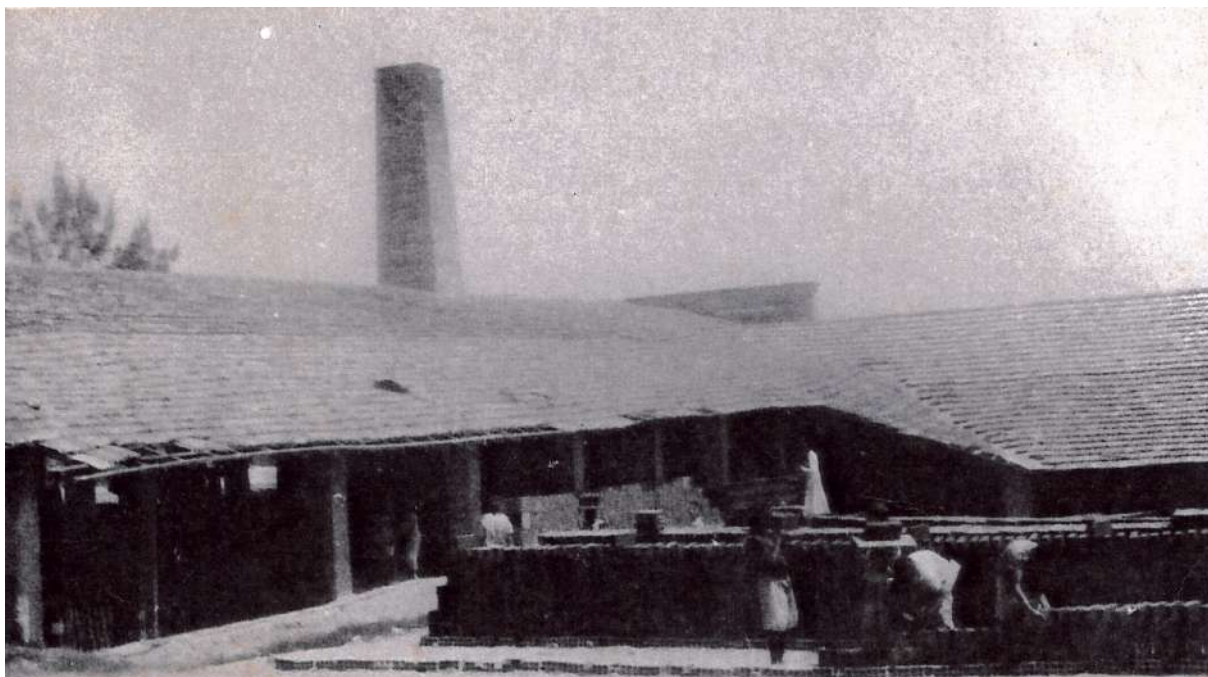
Empilhamento de tijolos para secagem antes da construção do telhado.
